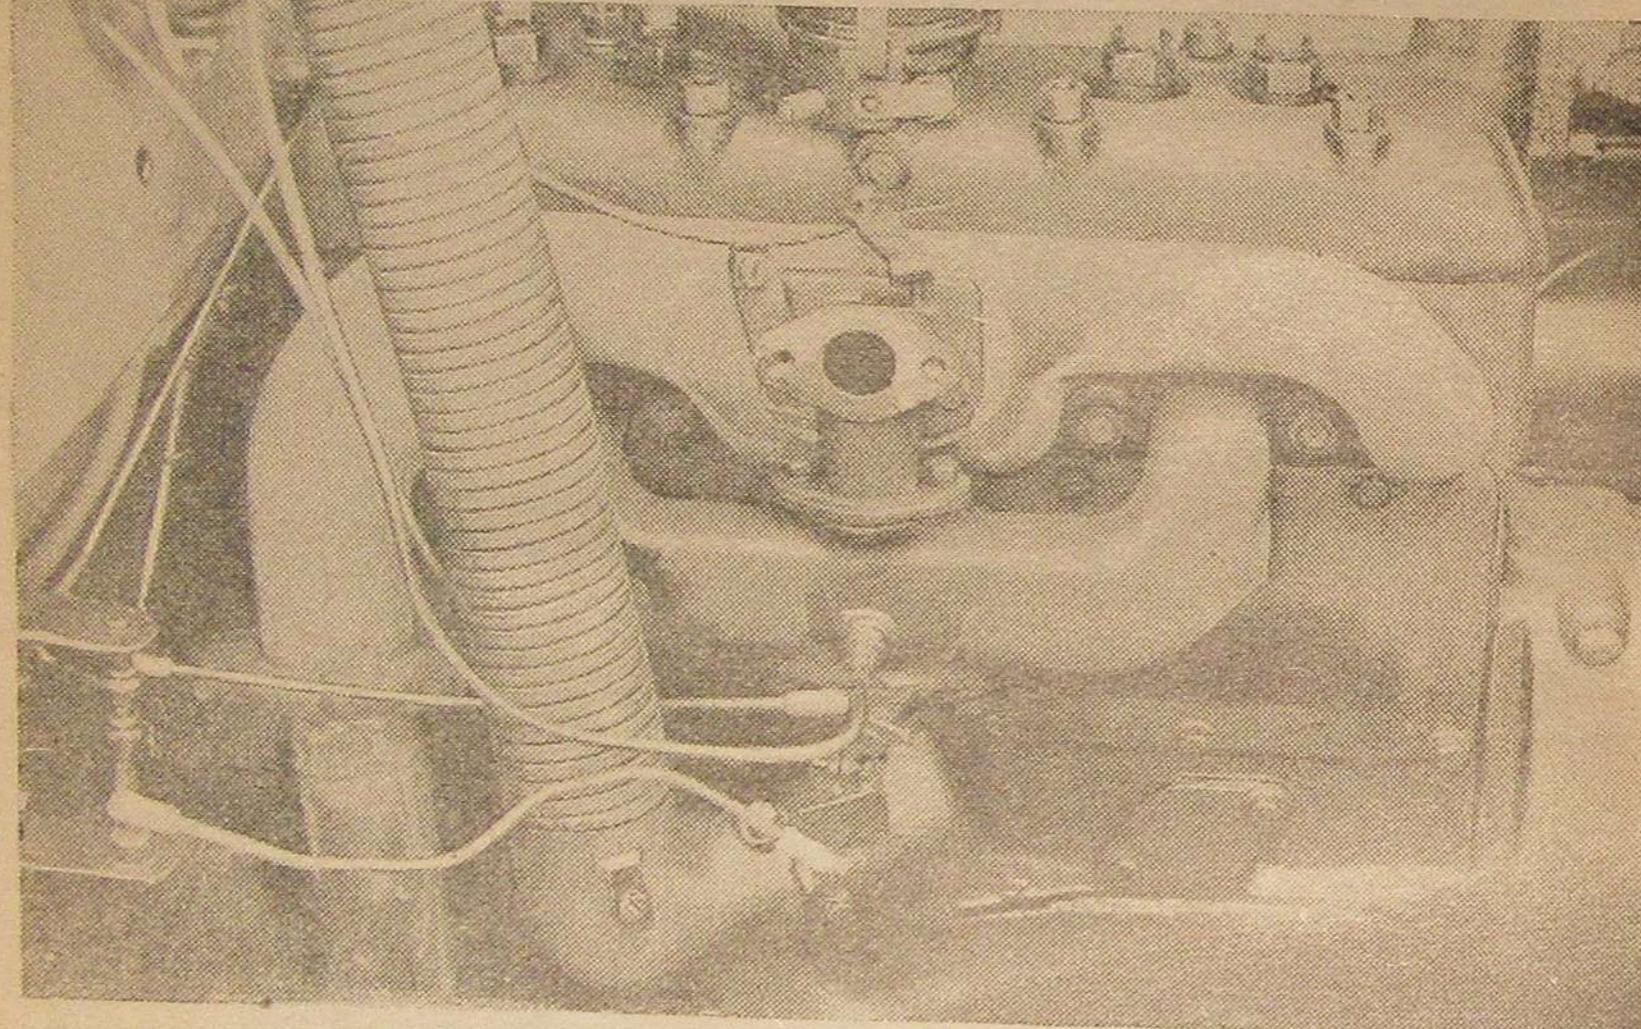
Газогенераторный двигатель М-1. Вид со стороны всасывающего коллектора
